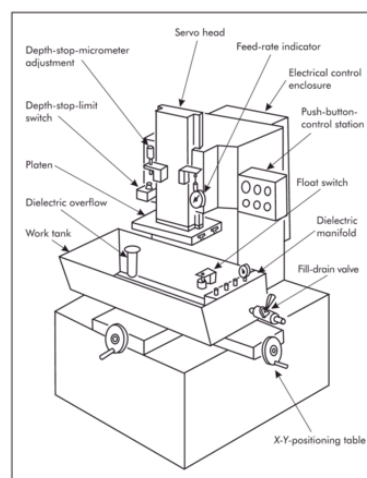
Eixos de posicionamento das máquinas de eletroerosão por penetração.
